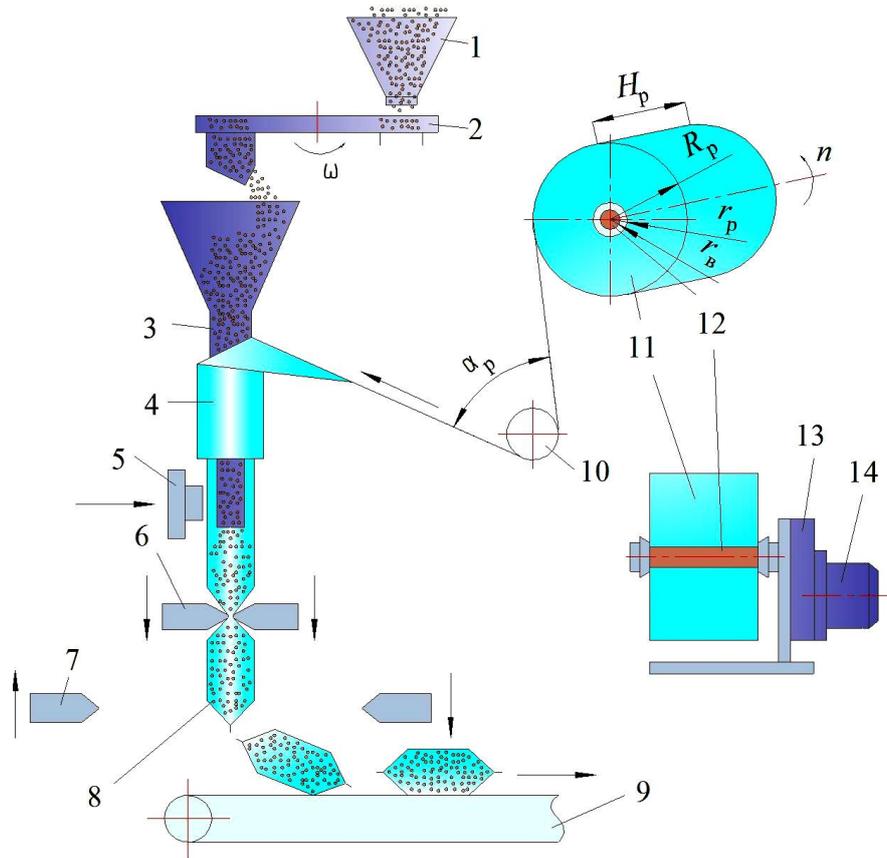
Технологическая и расчетная схема фасовочно-упаковочного автомата: 1 – загрузочный бункер; 2 – вращающийся дозатор; 3 – воронка; 4 – рукавообразователь; 5, 6, 7 – устройства для термосваривания продольного и горизонтальных швов; 8 – пакет с продуктом; 9 – конвейер; 10 – направляющий ролик; 11 – рулон ленты; 12 – вал; 13 – редуктор; 14 – двигатель
